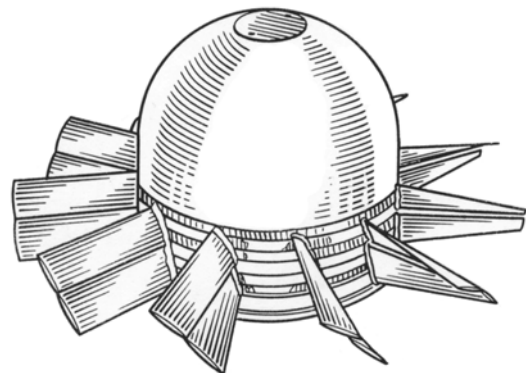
Робоче колесо осьового компресора з дворядними лопатковими вінцями
